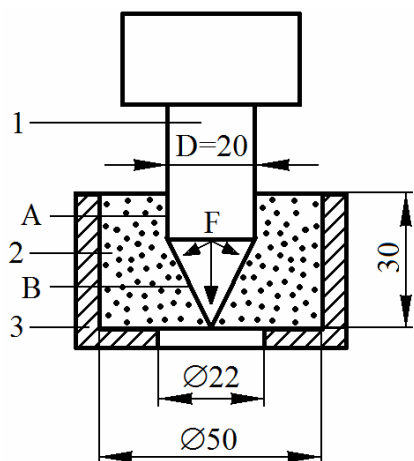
Схема испытания образцов стержневых и формовочных смесей
